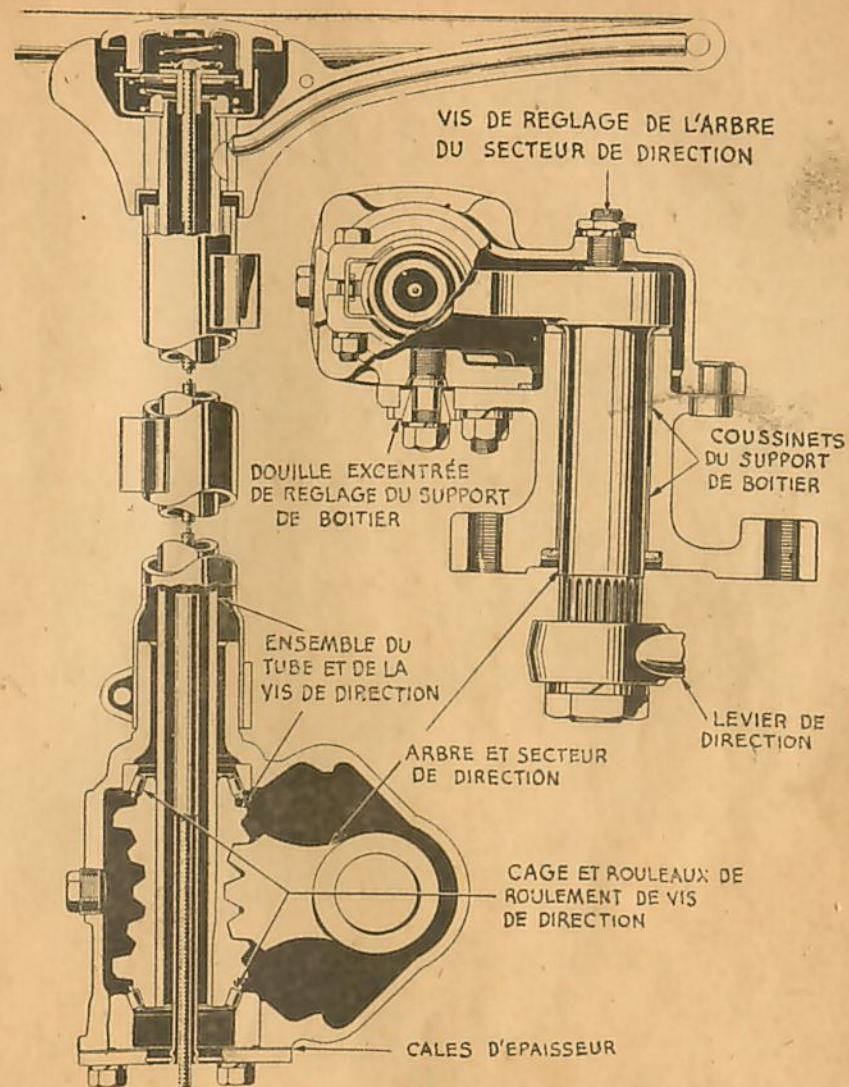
Vue en coupe du boîtier et de la colonne de direction.
